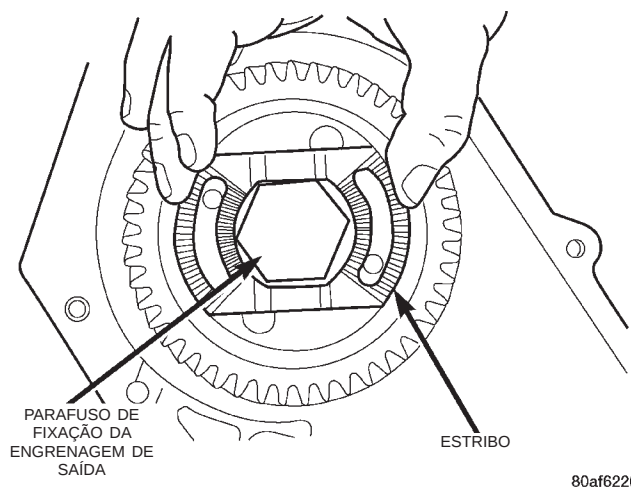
Estribo do Parafuso de Fixação da Engrenagem de Saída (Lado Dentado para Fora)
